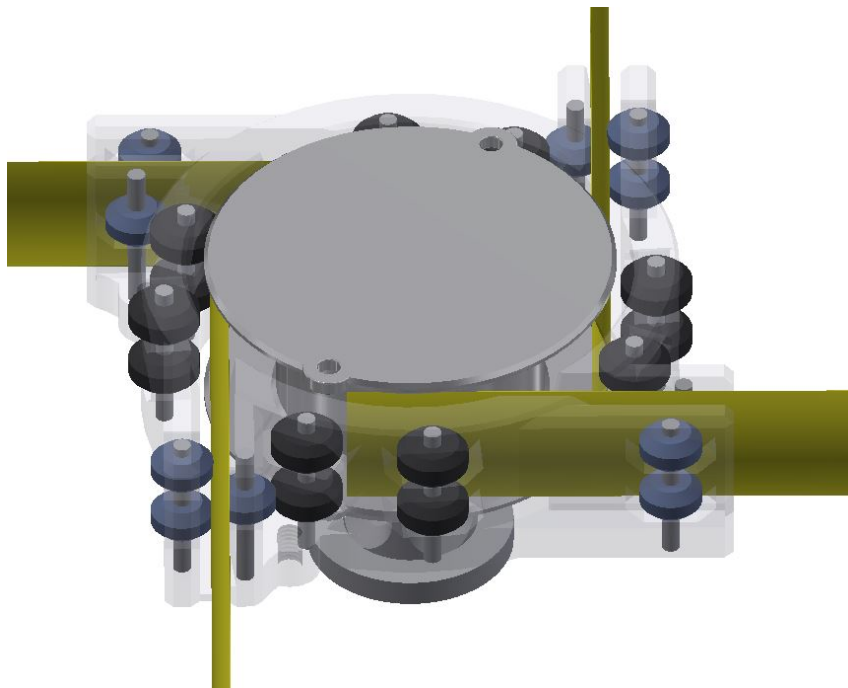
Vista de posición de rodillos y ejes dentro de la pieza
